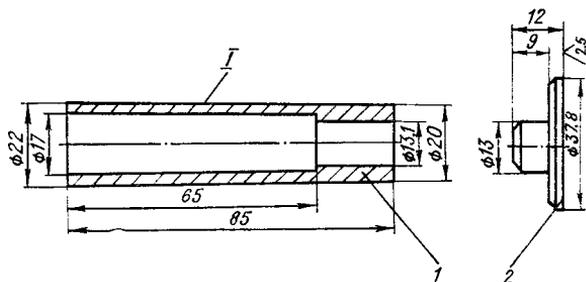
Приспособление для сборки циркуляционного (водяного) насоса:
